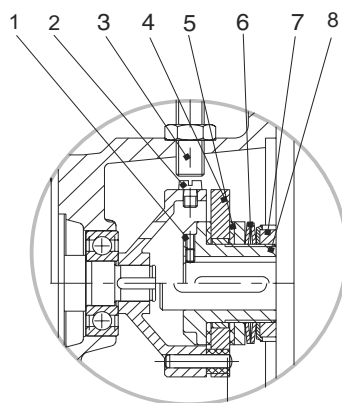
Inspeccionar / substituir os revestimentos de fricção 51472AXX
